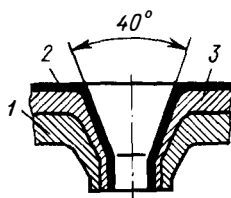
Соединение лепестка с листовым корпусом холодной сваркой:
